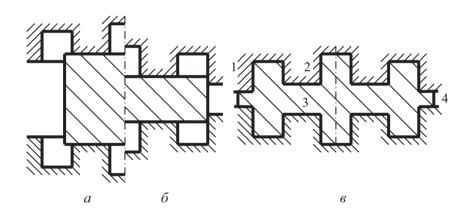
Формоизменение заготовки при получении поковки типа шестерни в штампе с горизонтальным разъемом:
